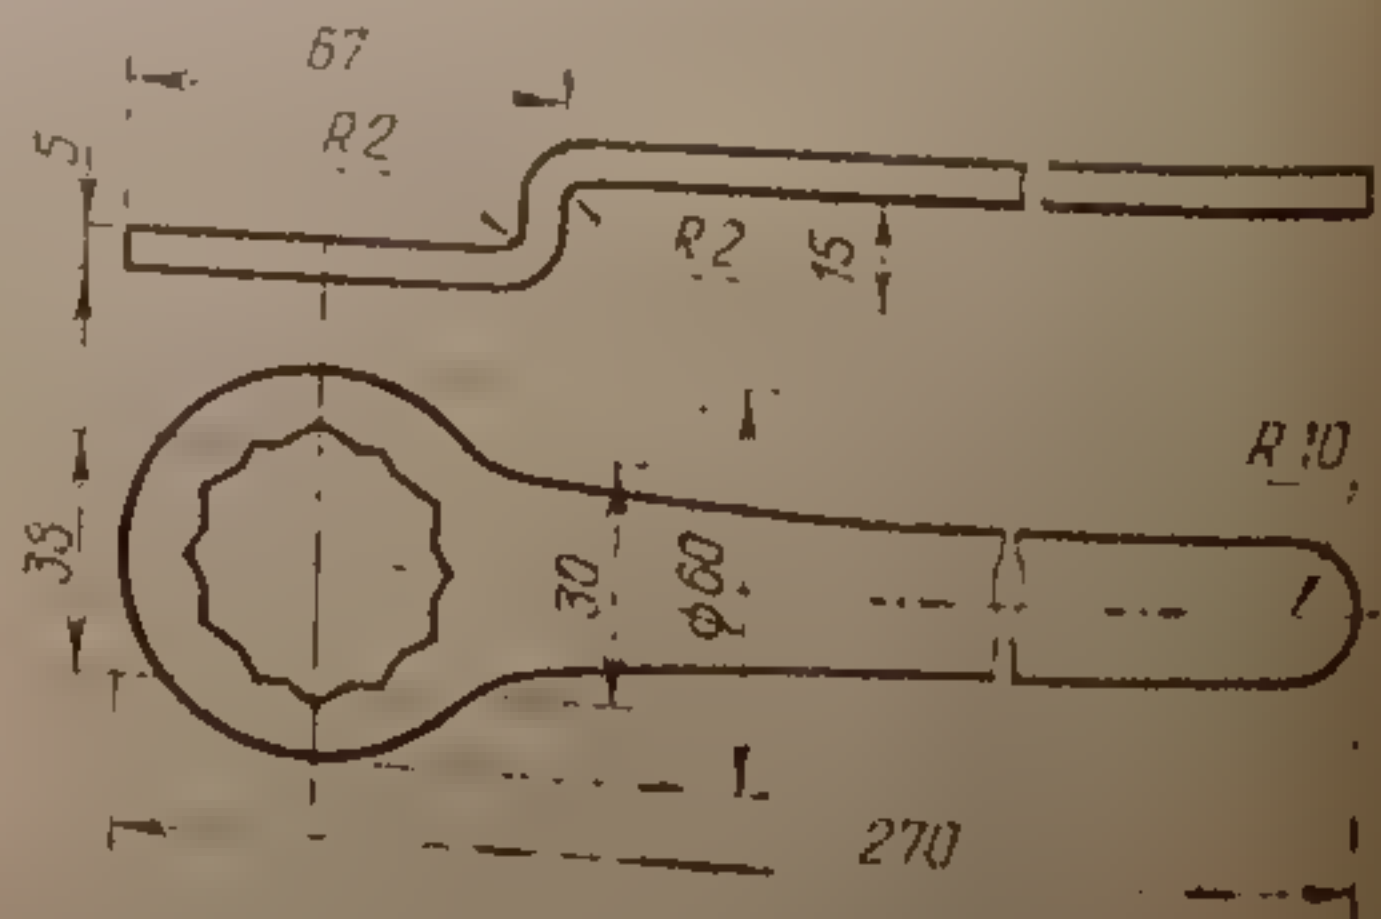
Ключ для поворота коленчатого вала двигателя ВАЗ-2105 и 2107.
